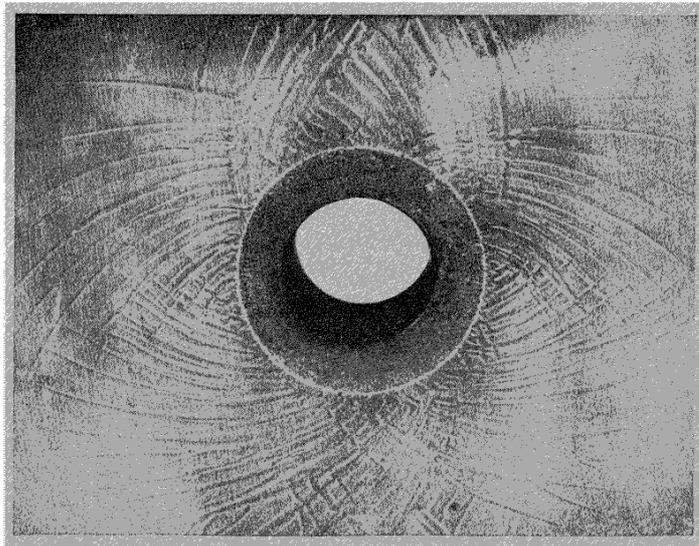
Lignes de Piobert produites, sur la seconde face d'une barre de fer, par le poinçonnage d'un trou.
